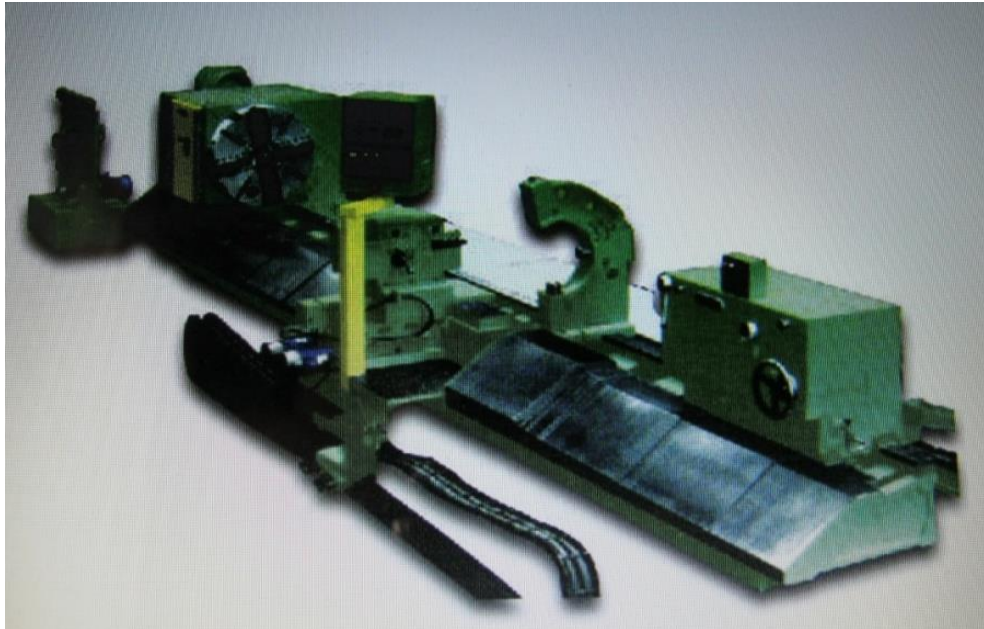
Загальний вид верстату мод. 1Д655Ф3
